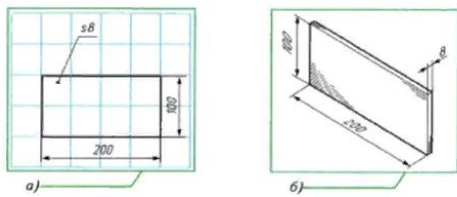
Эскиз (а), чертежи (б) деталей швейного изделия
